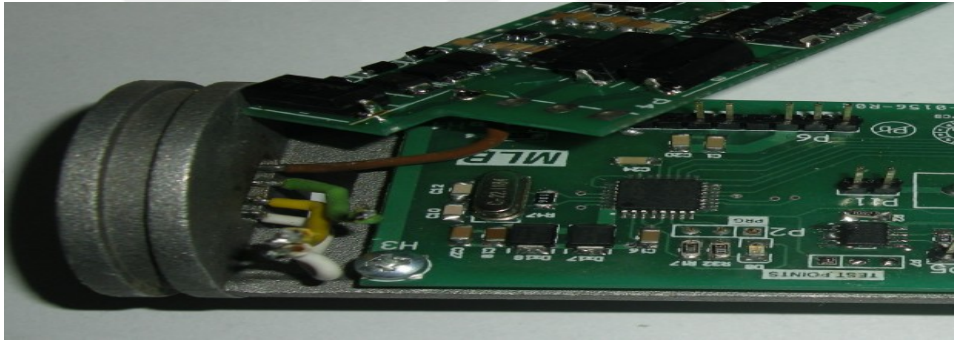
'te tasarlanan alt pcb kartının prob başlığına montajlanması verilmiştir.
